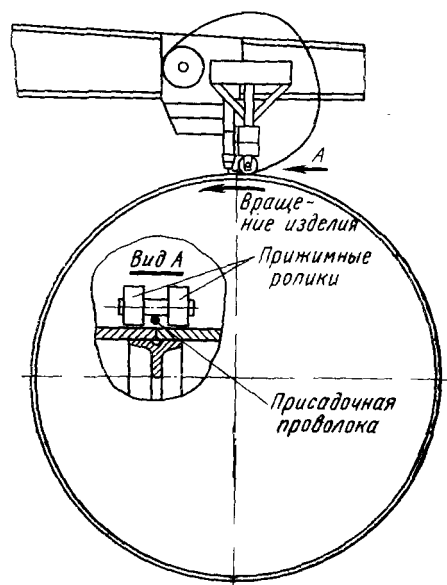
Схема приспособления для прижатия кромок к подкладному кольцу перед сварочной головкой
